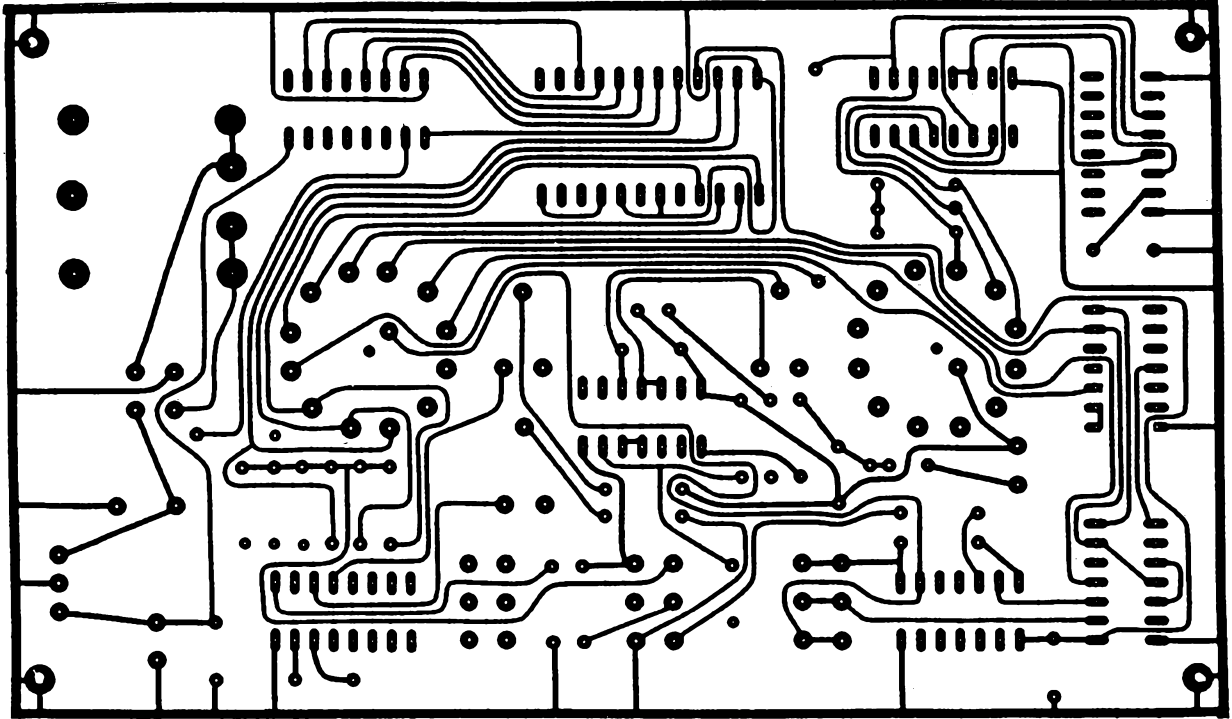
De soldeerzijde van de dubbelzijdige print.
